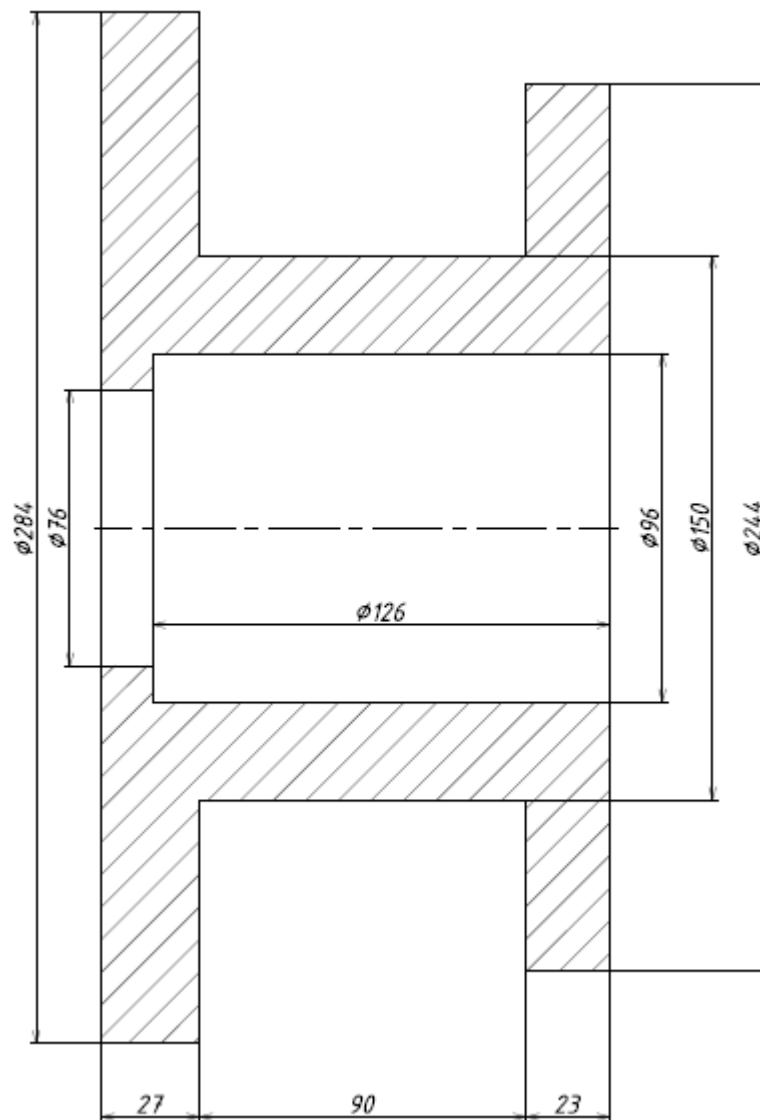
Заготовка деталі «Корпус підшипника»
